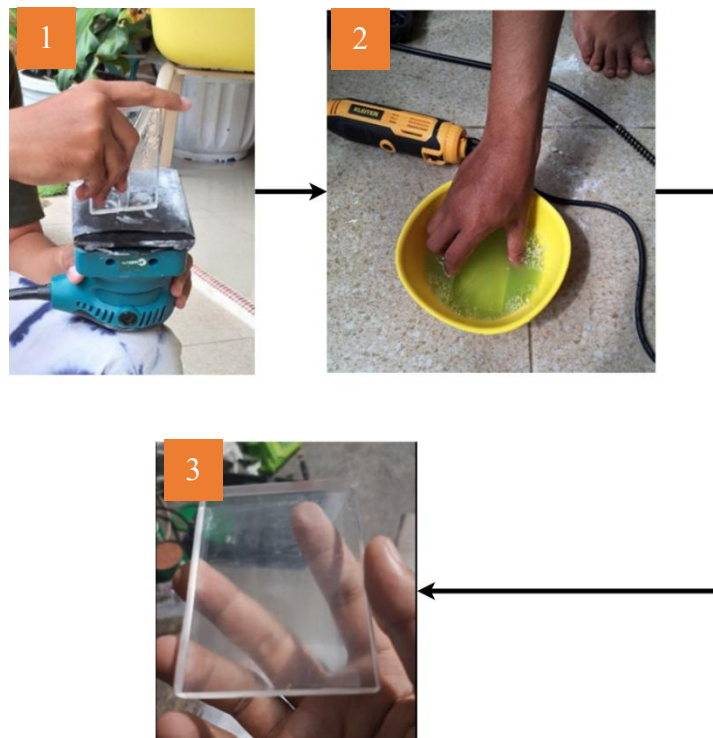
12 Hasil permesinan CNC milling 3-Axis
